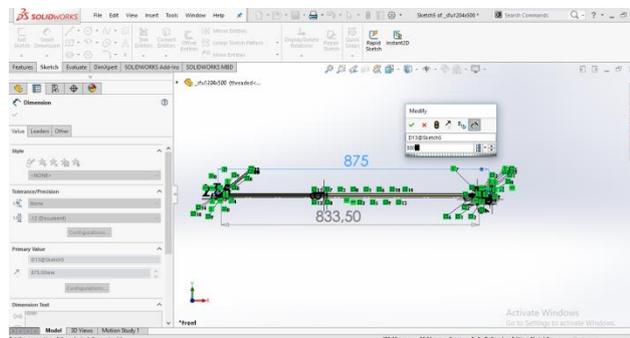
Desain Komponen *Ballscrew Kit
